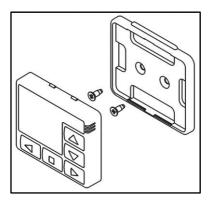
Installation de la centrale PU-27 à l'aide d'un Support de montage.
